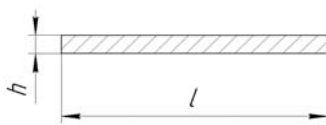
Вихідна заготовка, відносно якої ведеться розрахунок
